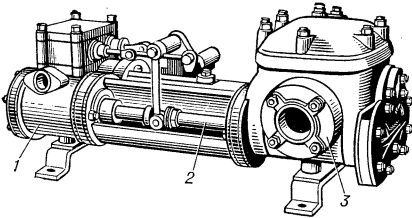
Паровой прямодействующий поршневой двухцилиндровый насосный агрегат системы Вортингтона в современном исполнении: 1 — блок с цилиндрами и клапанами поршневого насоса; 2 — шток, соединяющий поршни насоса и парового двигателя; 3 — блок с цилиндрами и золотниками паровой машины.
